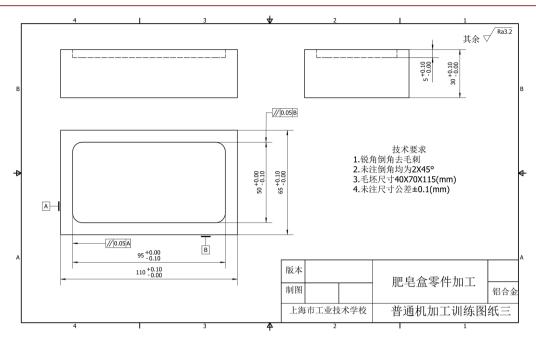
Inner contour machining training project drawing 图 3. 内轮廓加工训练项目图纸
